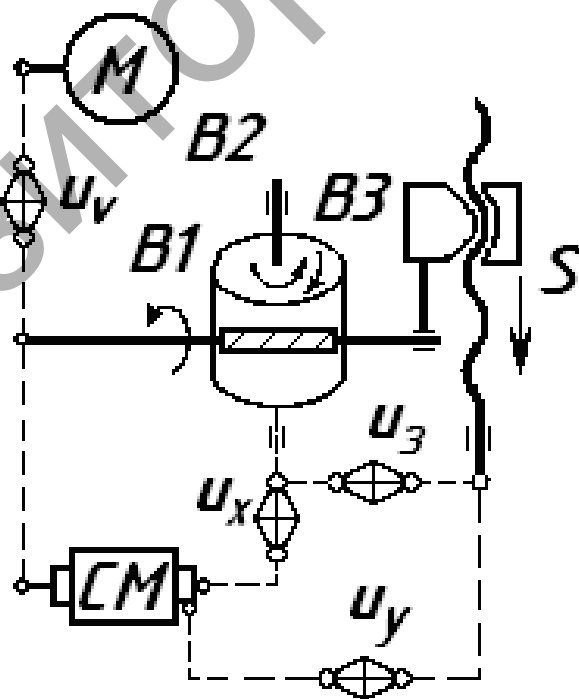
Структурная кинематическая схема зубофрезерного станка
